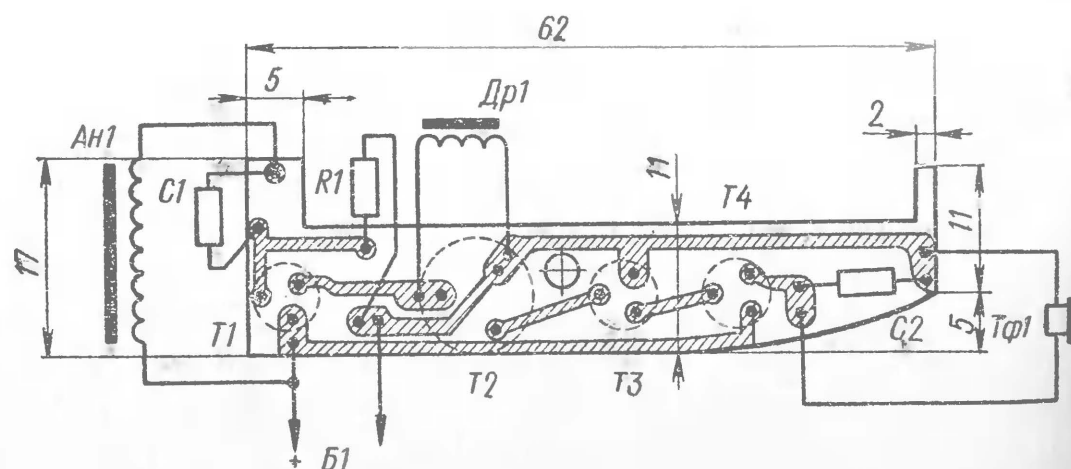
Чертеж печатной платы и расположение на ней деталей
